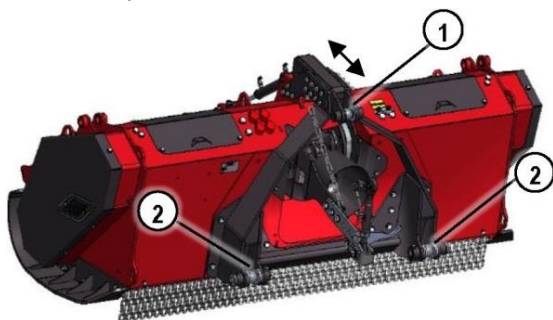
Точки крепления мульчирующей фрезы при трехточечном креплении
